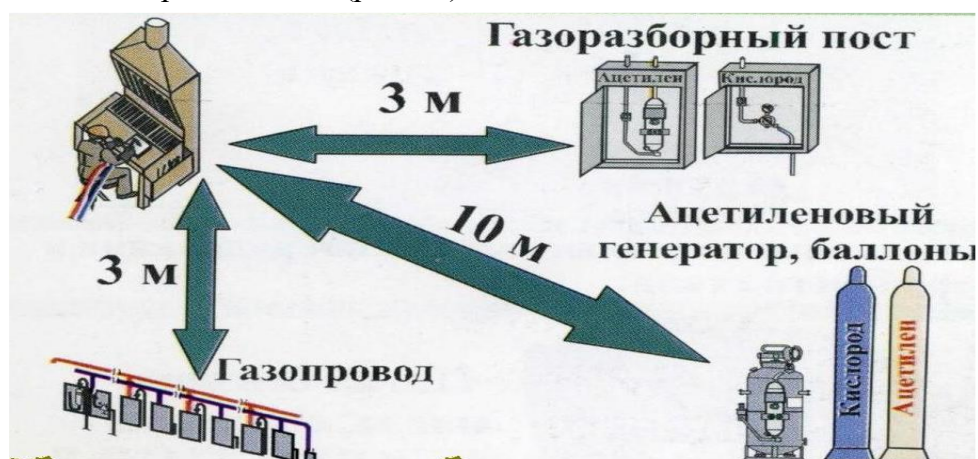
Правила безопасности установки и размещения баллонов с газами на стационарных постах при газовой резке и сварке металлов
